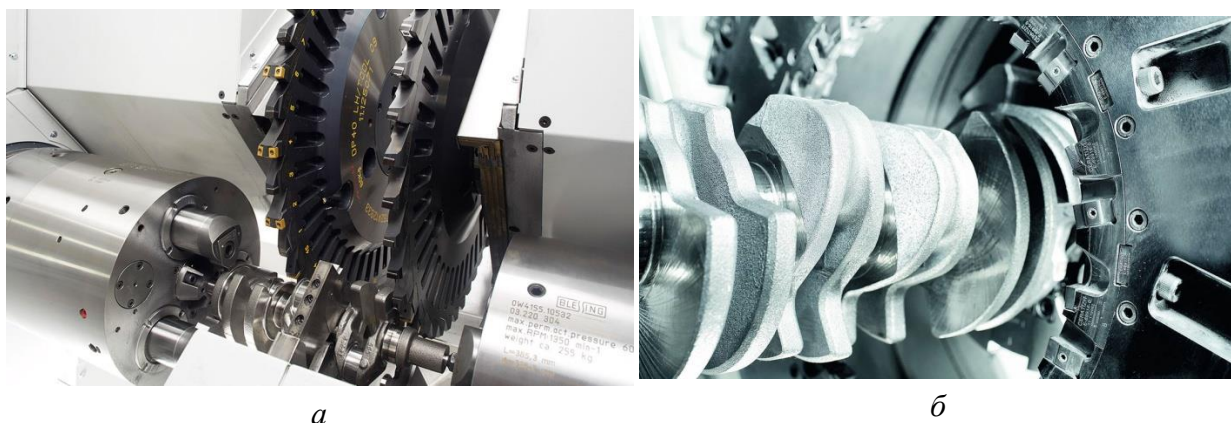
Фрезерування колінчастих валів фрезою з розташуванням пластин ззовні (а) та всередині (б) [14]
